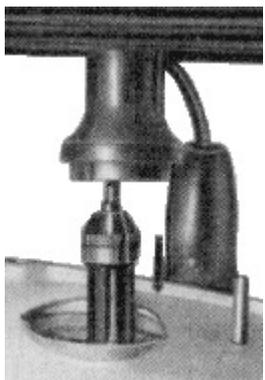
Gummischutzhauben für Bowdenzugaufnahmen
